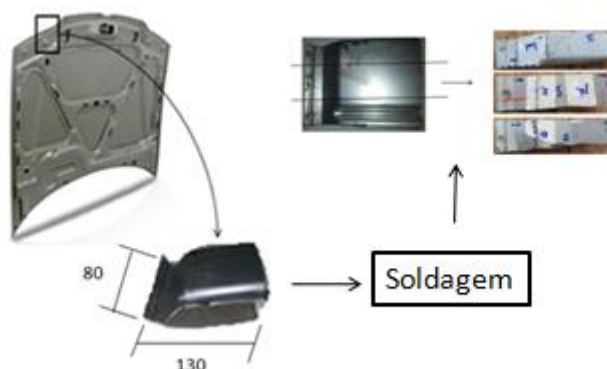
Ilustração da origem das amostras, soldagem e corte da junta soldada. (TOLENTINO, SAHATDJIAN, *et al.*, 2013)
